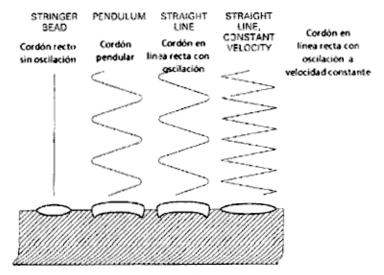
Oscilaciones y Penetración de Cordones de Soldadura y efectos de dilución
